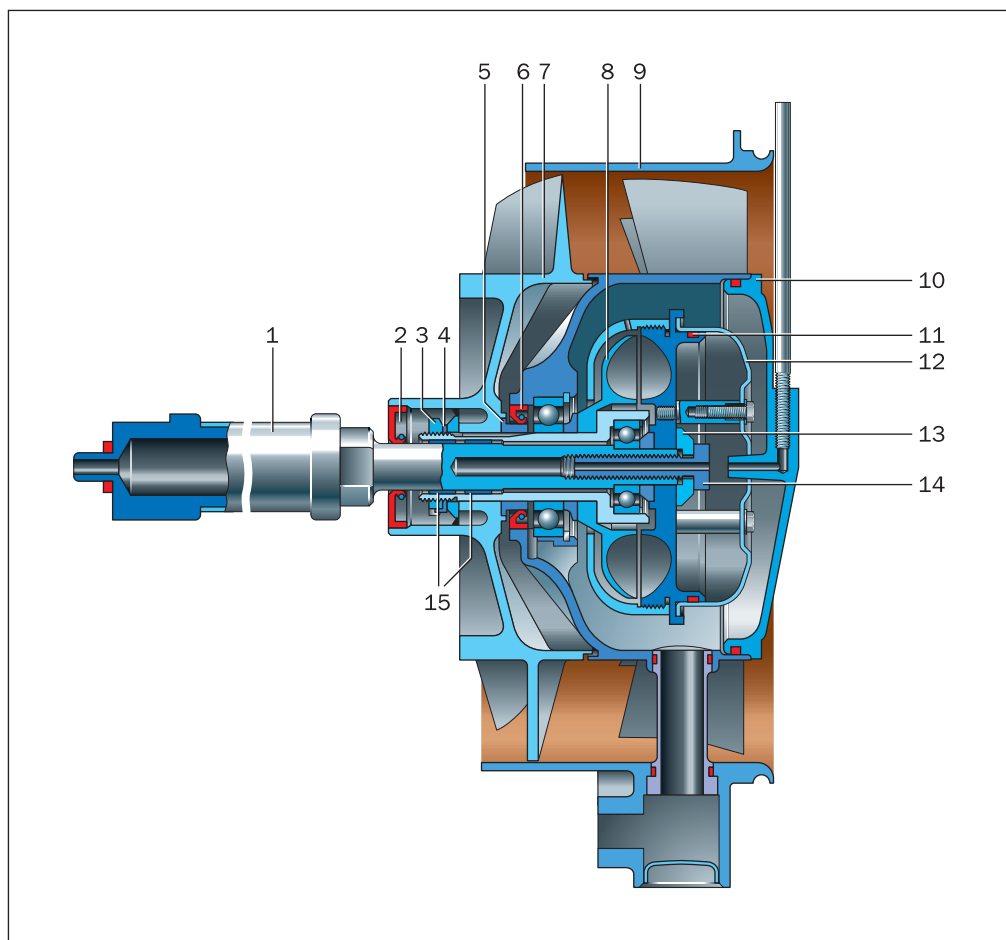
Установка гидравлической муфты в приводе вентилятора: 1 — вал привода вентилятора; 2, 6 — сальники (манжеты); 3 — гайка вала; 4 — стопорная шайба; 5 — втулка сальника; 7 — рабочее колесо; 8 — гидромуфта; 9 — корпус вентилятора; 10 — крышка; 11 — уплотнительное кольцо; 12 — корпус центрифуги; 13 — шайба; 14 — маслопроводный болт; 15 — подшипник скольжения
